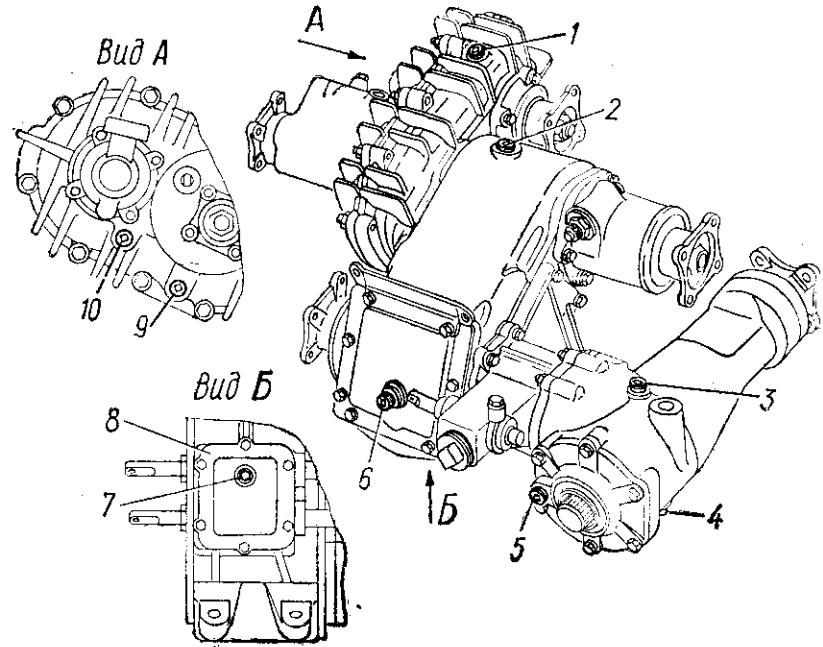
Расположение пробок контрольных, заправочных и сливных отверстий в раздаточной коробке в сборе с редуктором и коробкой отбора мощности на дополнительные колеса:
